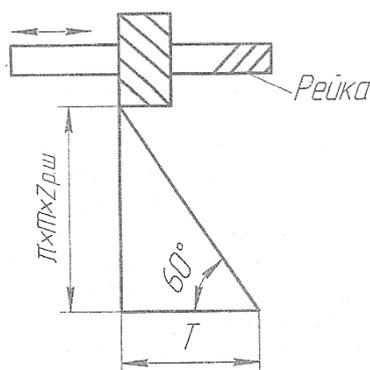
Развертка винтовой линии зуба реечной шестерни
